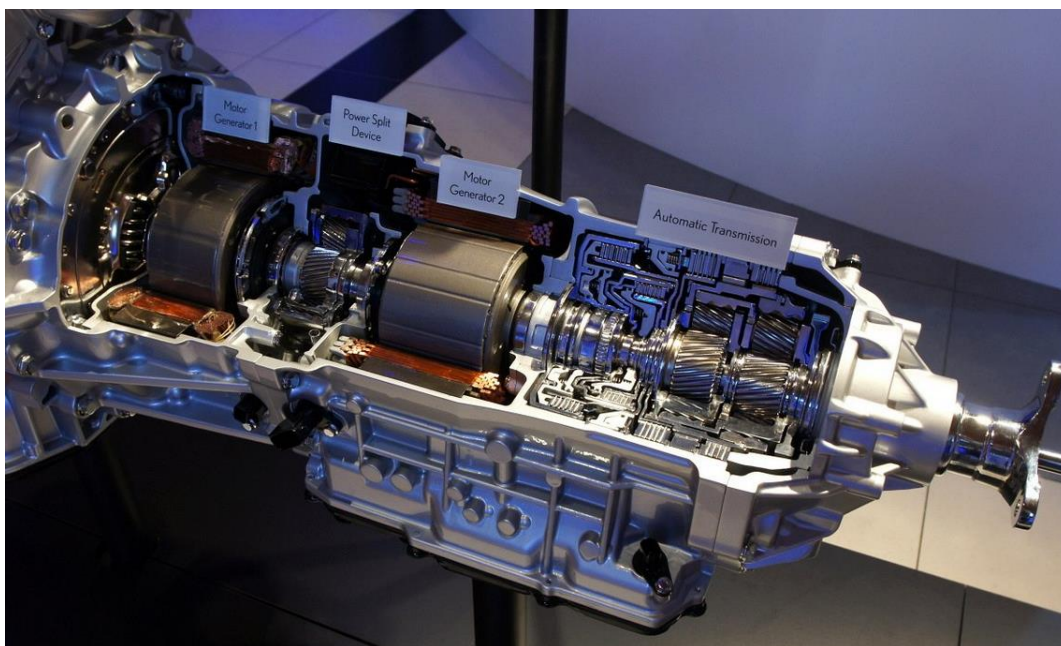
Uspořádání převodovky u Lexus GS 450h [106]
